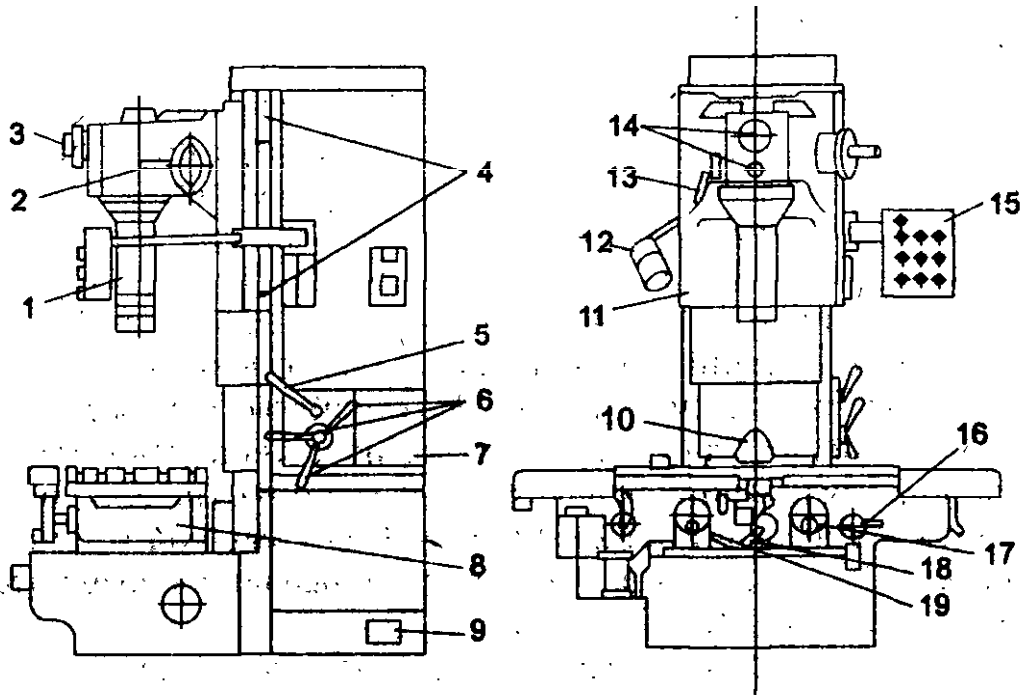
Общий вид и органы управления станка для растачивания цилиндров:
